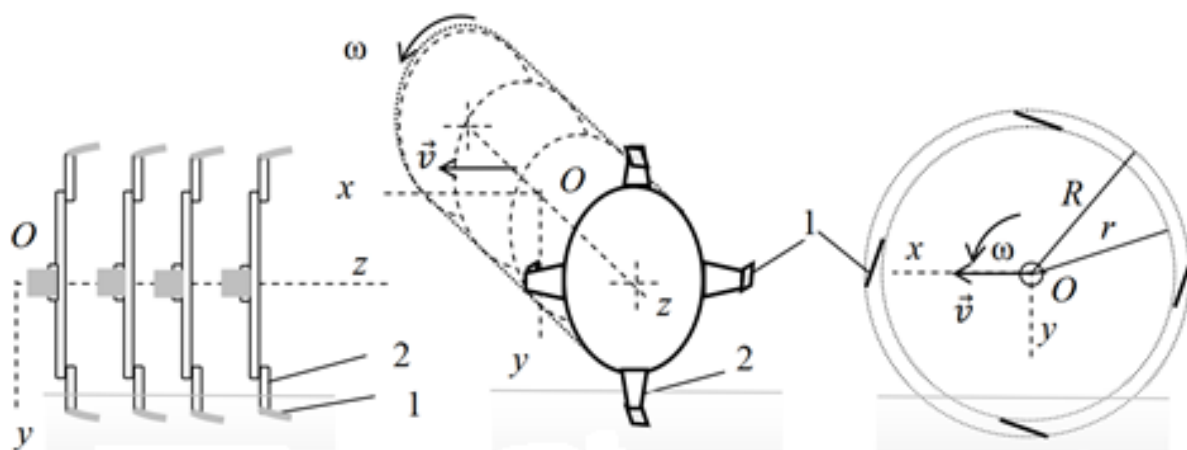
Схема барабана фрезы с режущими ножами и боковинами
